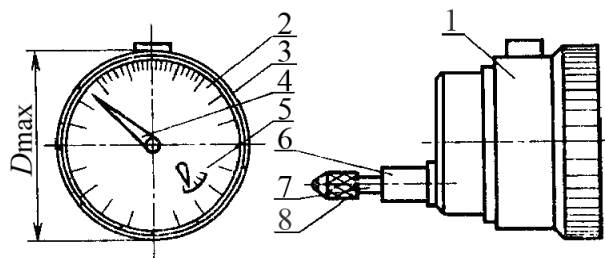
Внешний вид и основные размеры индикатора типа ИТ:
